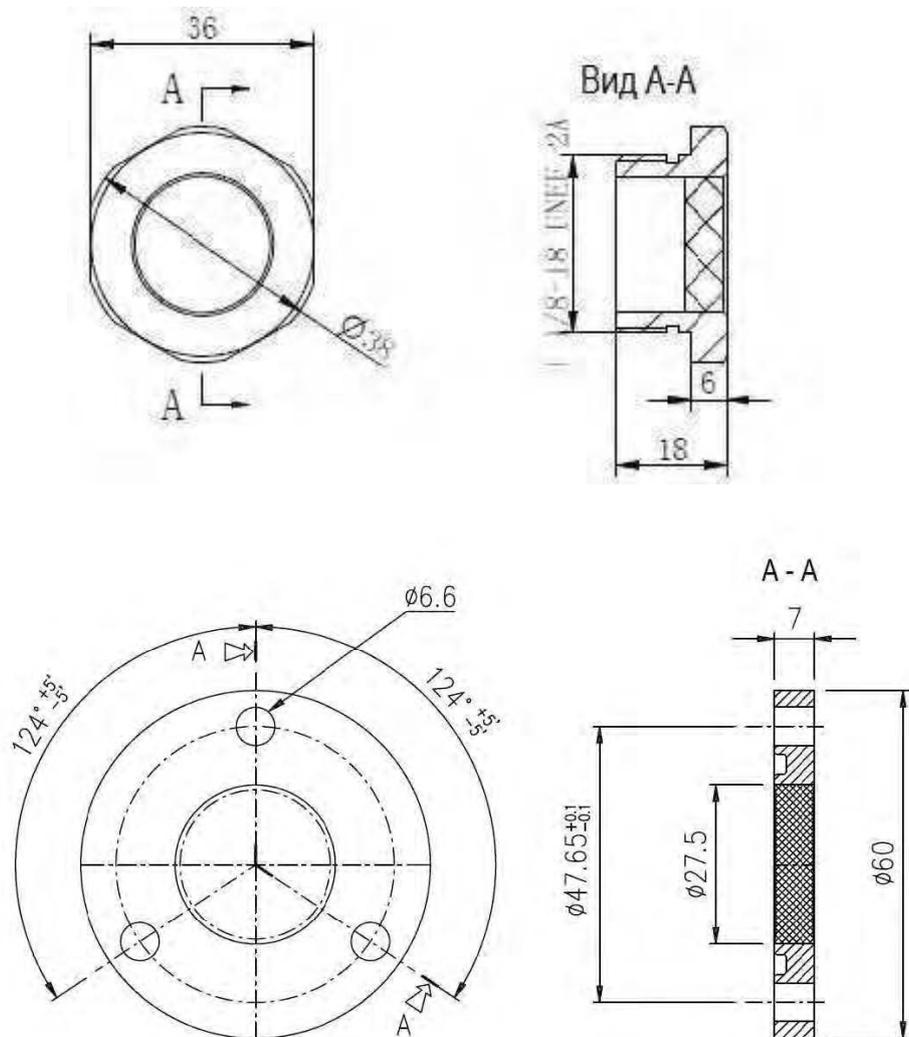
Габаритный чертеж маслосмотрового стекла
